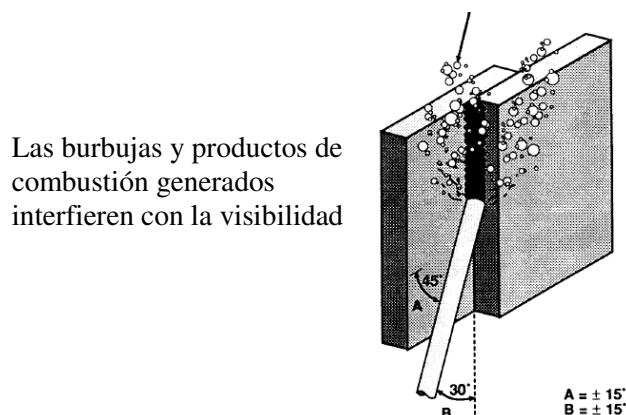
Técnica de autoconsumo en soldadura MMA, para soldadura de filetes en posición vertical [7].
